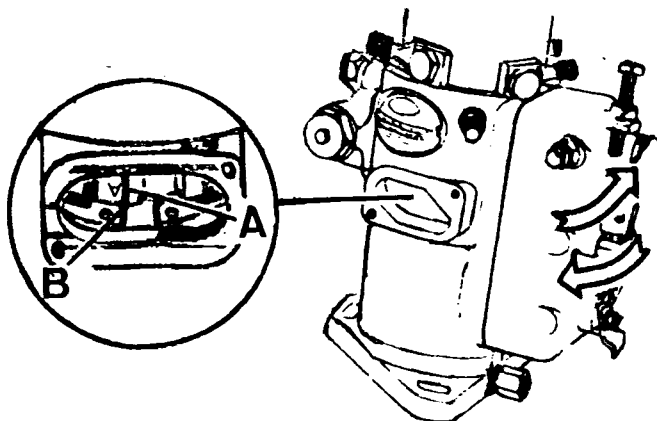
Ajuste de la bomba una vez montada en el motor
